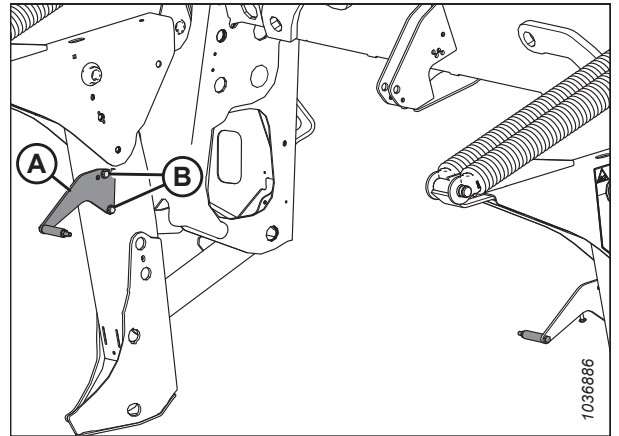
Кронштейн формовочного щитка — серия R2
